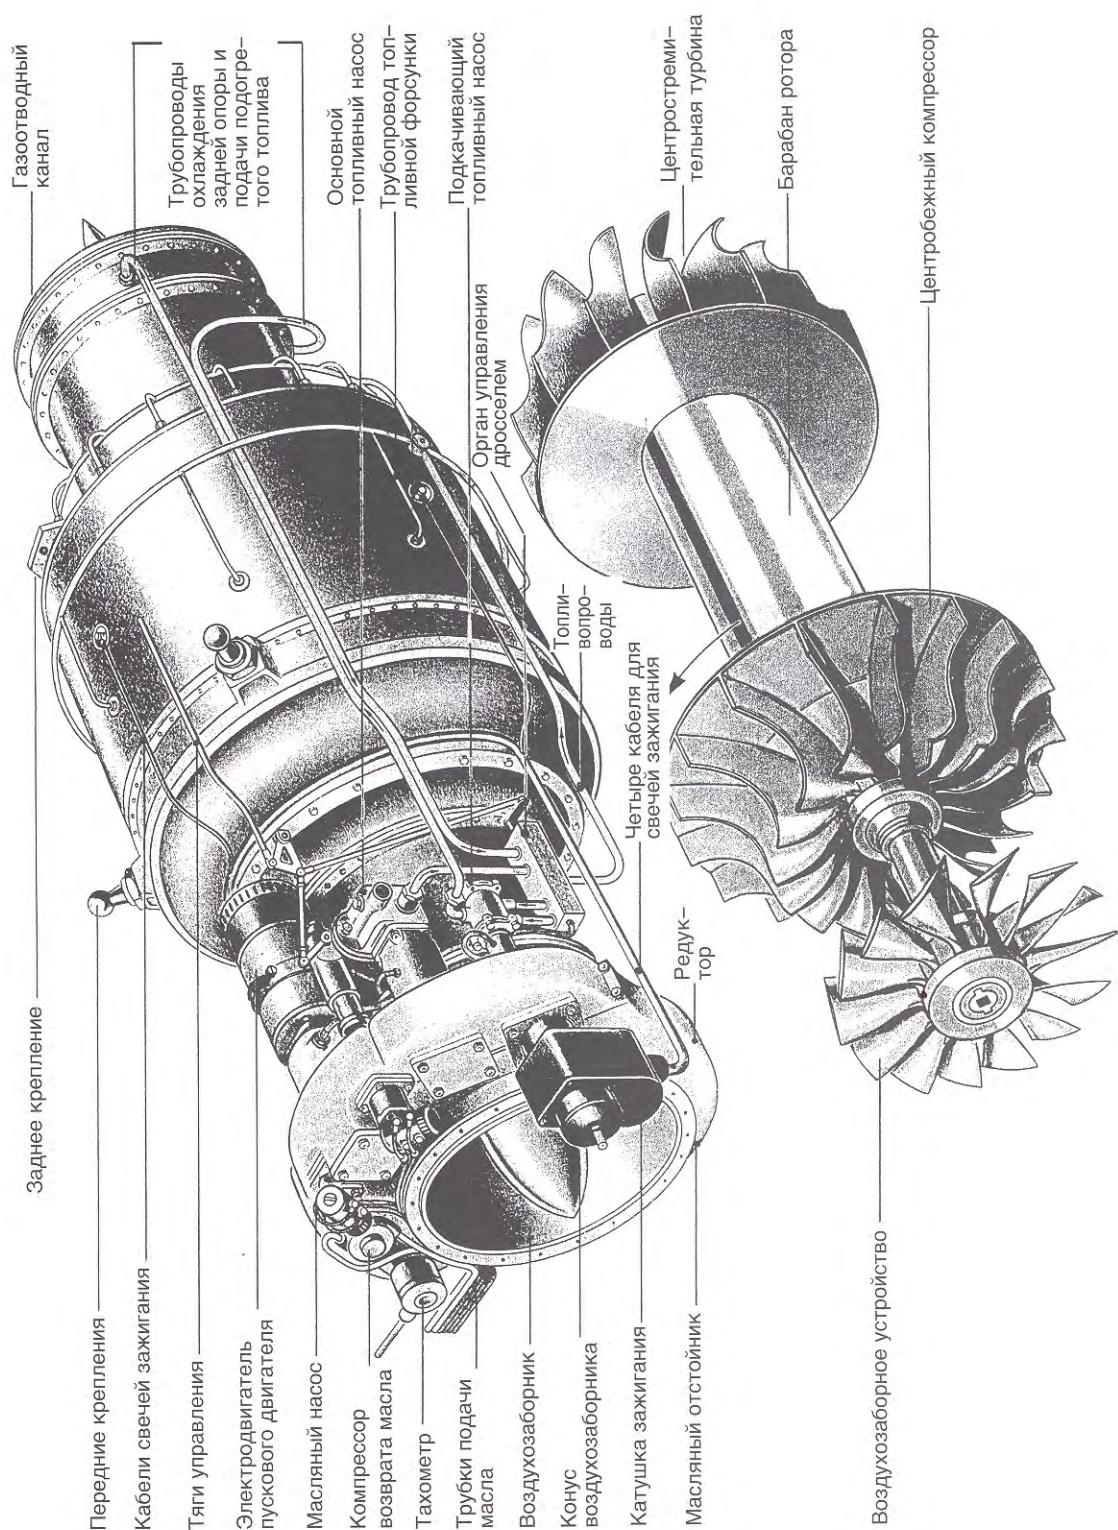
Общий вид турбореактивного двигателя HeS 8A
